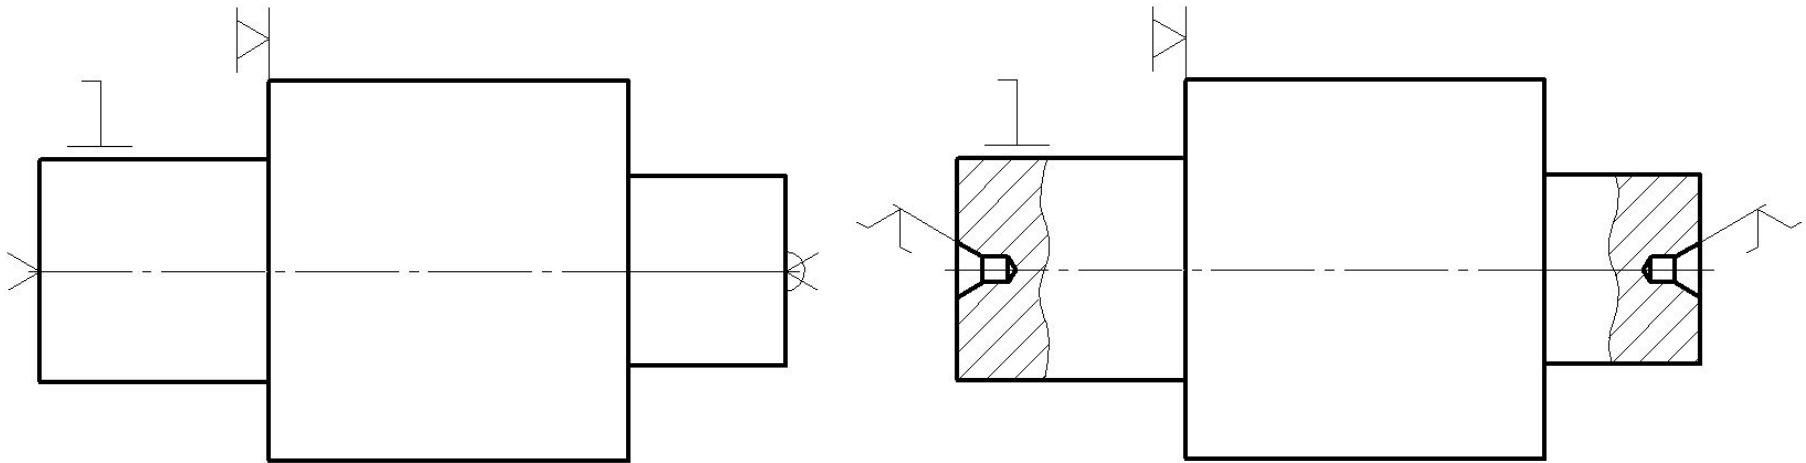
Установка заготовки центра + поводковый патрон на технологическом эскизе
